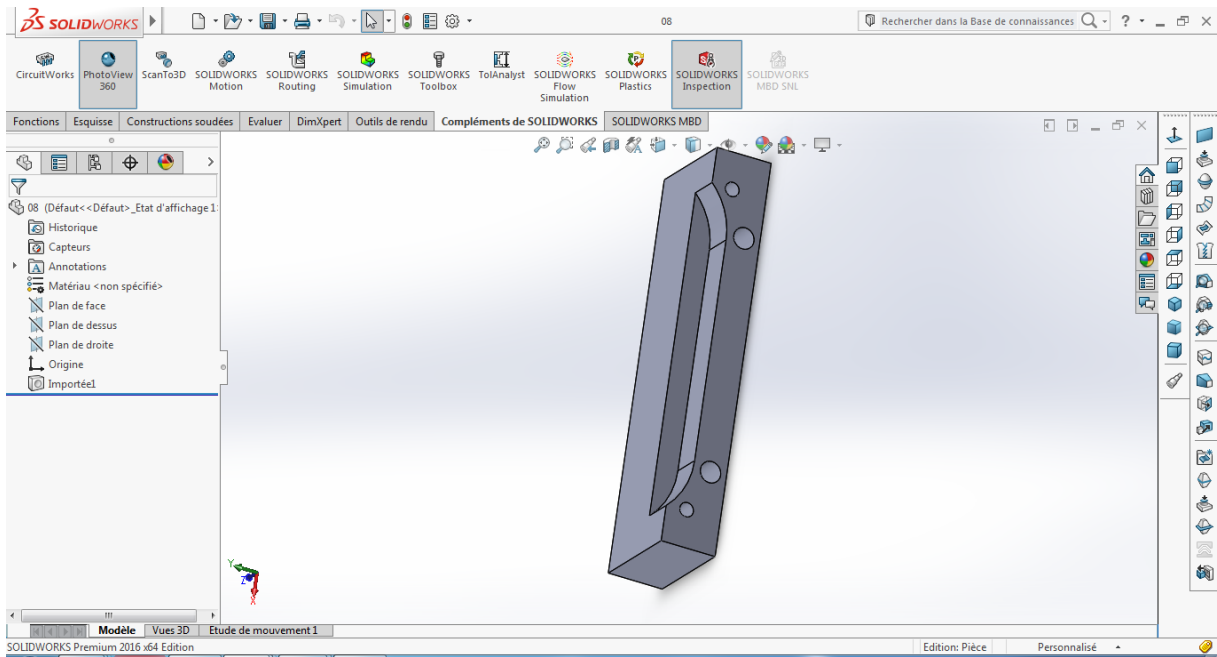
Cassette coté femelle de coupe sur plan de surface)
